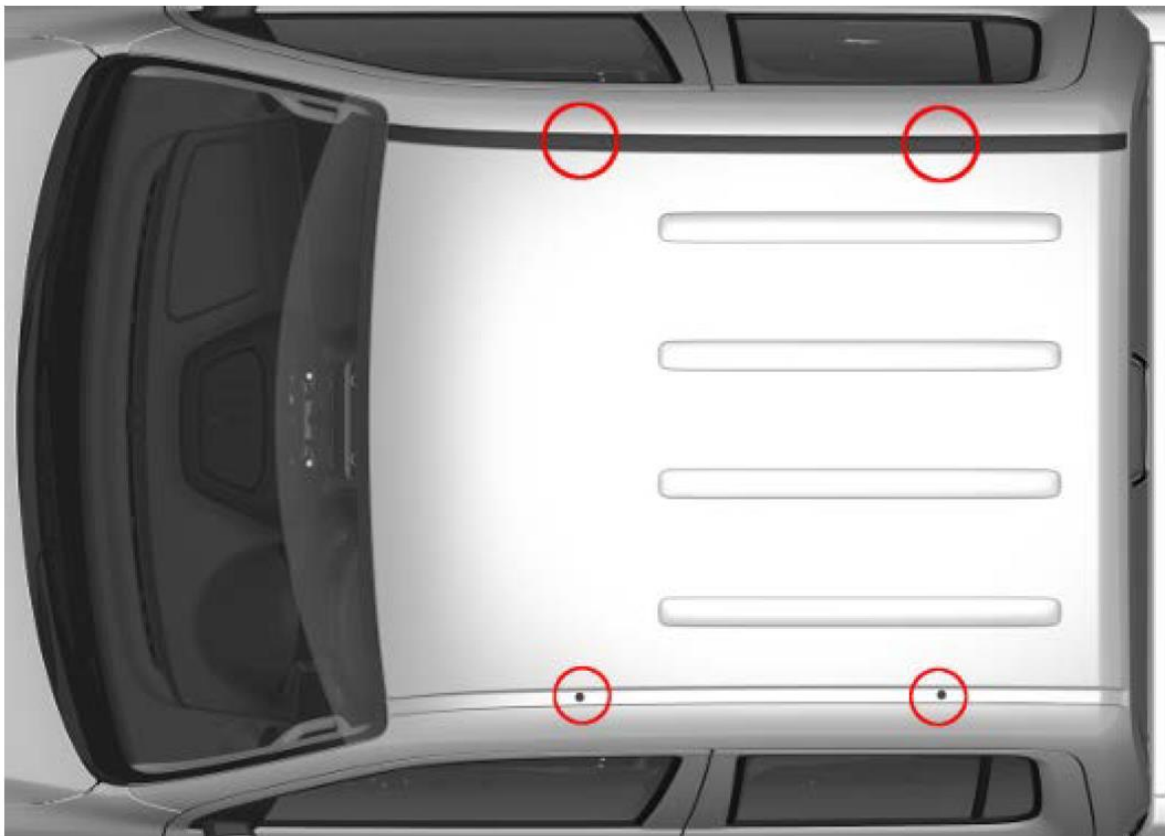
Anschraubpunkte Dachgepäckträger Amarok-DC (rot markiert!)
